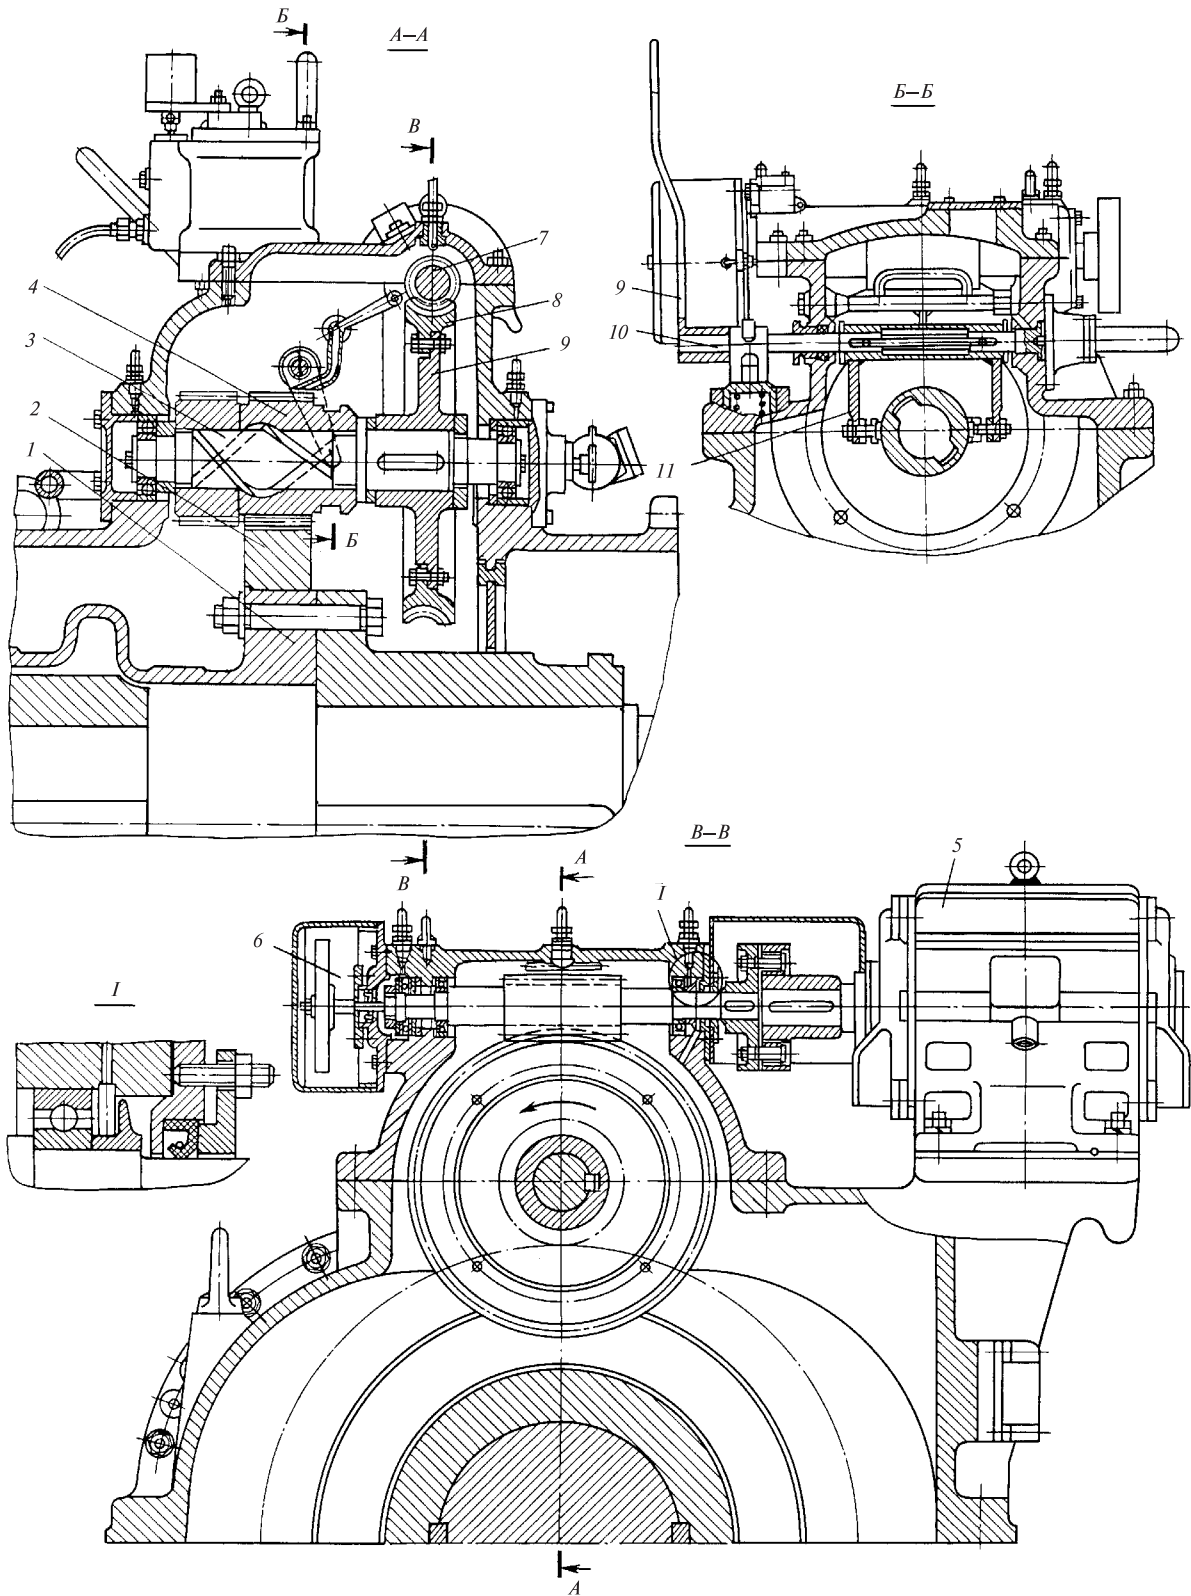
Валоповоротное устройство турбин ТМЗ
